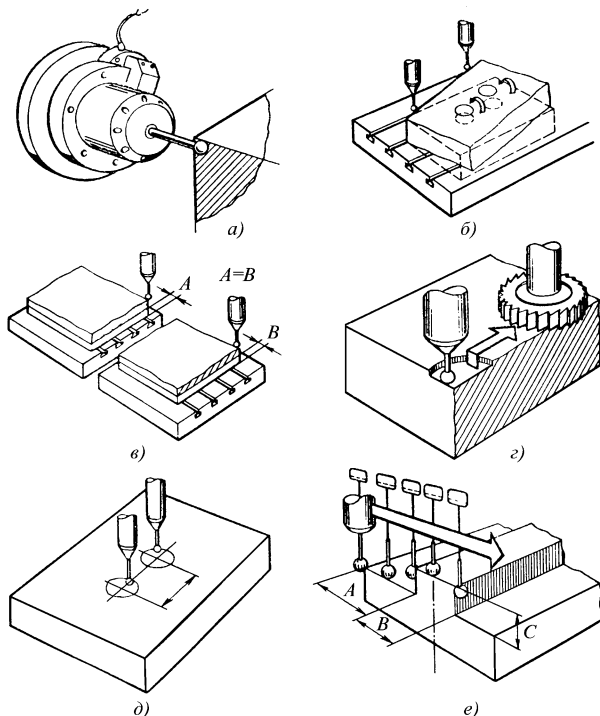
Схемы контроля деталей щуповой головкой:
